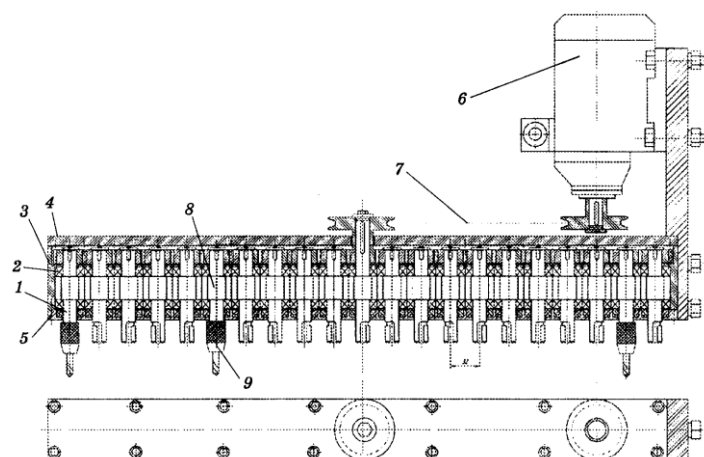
Багатошпindelьна головка: 1 – шпindelьні вали; 2 – кулькові підшипники; 3 – корпус; 4 – верхня кришка; 5 – нижня кришка; 6 – електродвигун; 7 – пасова передача; 8 – шестерні; 9 – патрони
